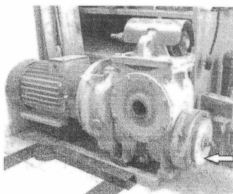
Дисковый тормоз ТДП-11, пристроенный к редуктору
